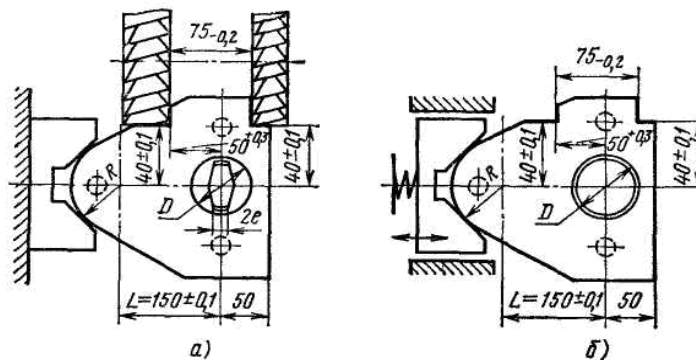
Схеми установки заготовки при фрезеруванні (до задачі 1.18)
